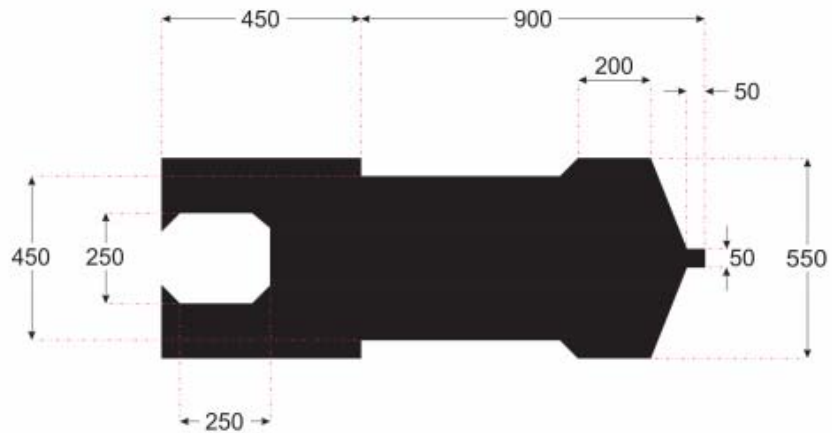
Dimensiones del interruptor presentado en [2] todas las dimensiones en μm
